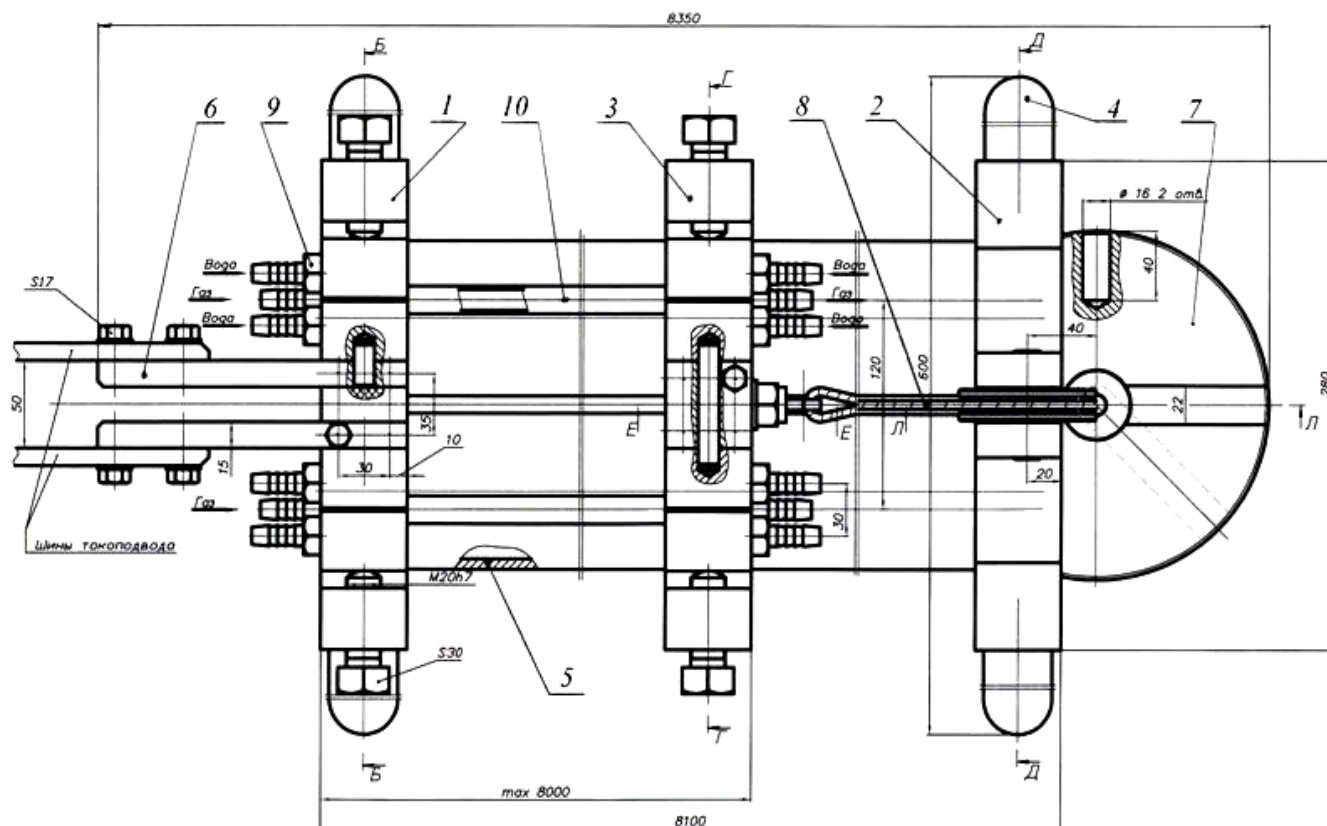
Чертеж общего вида (вид сверху) опытной установки электроконтактного нагрева труб: 1 – передняя поперечина; 2 – задняя поперечина; 3 – подвижная поперечина; 4 – опора; 5 – станина; 6 – шина токоподвода; 7 – пневматическое устройство натяжения; 8 – канат; 9 – штуцер системы охлаждения; 10 – нагреваемая труба
